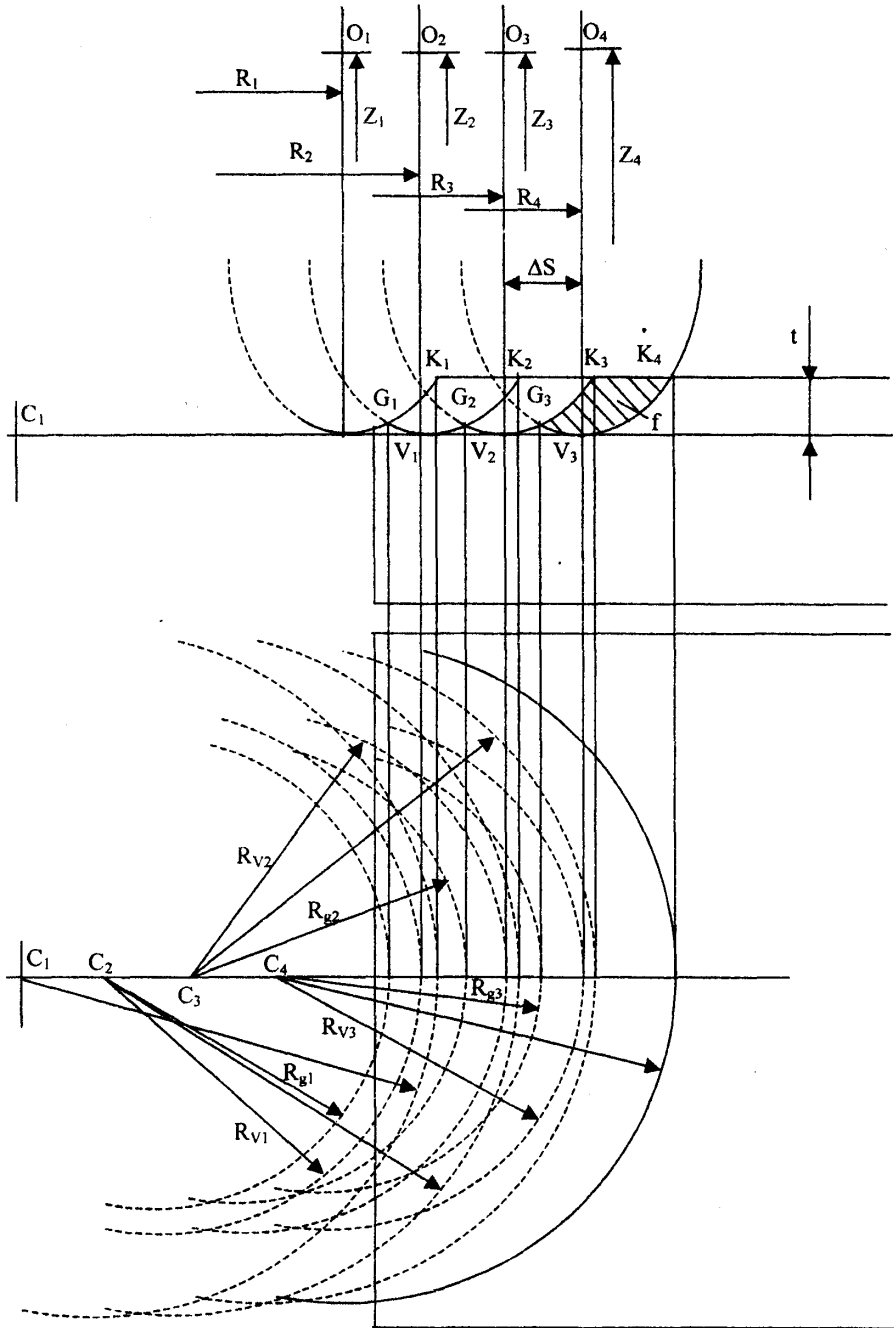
Утворення концентричних лунок на поверхні заготовки при наявності одного ножа еліптичної форми при відсутності похибок геометрії та кінематики фрези
